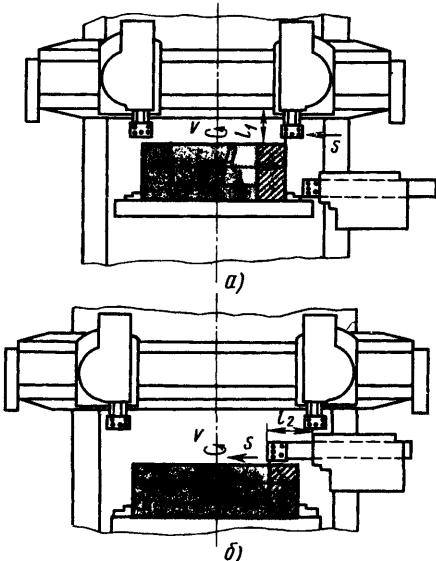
Схемы обработки торцевых поверхностей резцами вертикального (а) и бокового (б) суппортов
